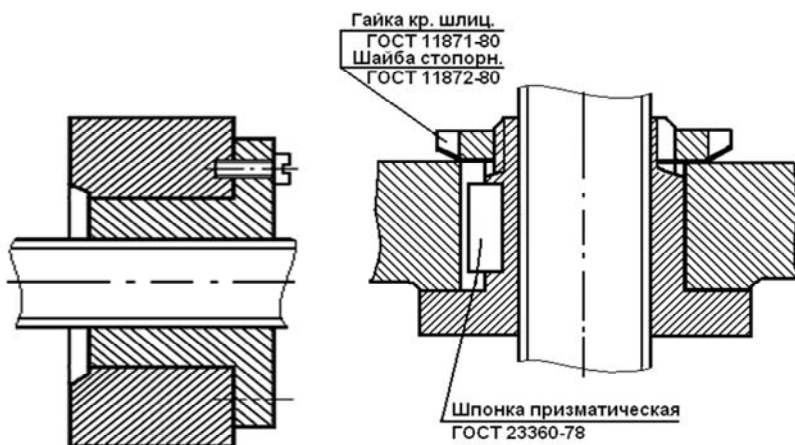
Невращающаяся гайка, установленная в корпус
